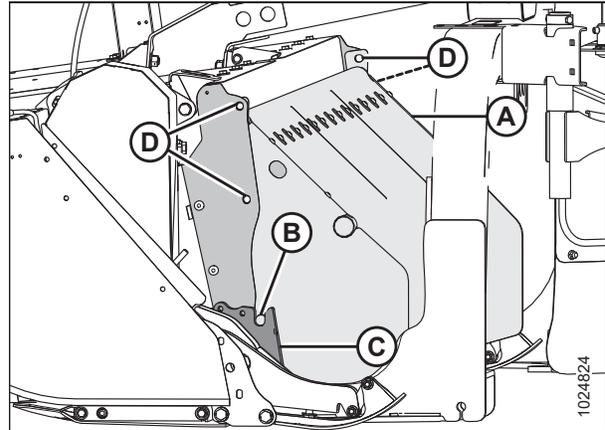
Левая сторона жатки — с правой стороны наоборот
